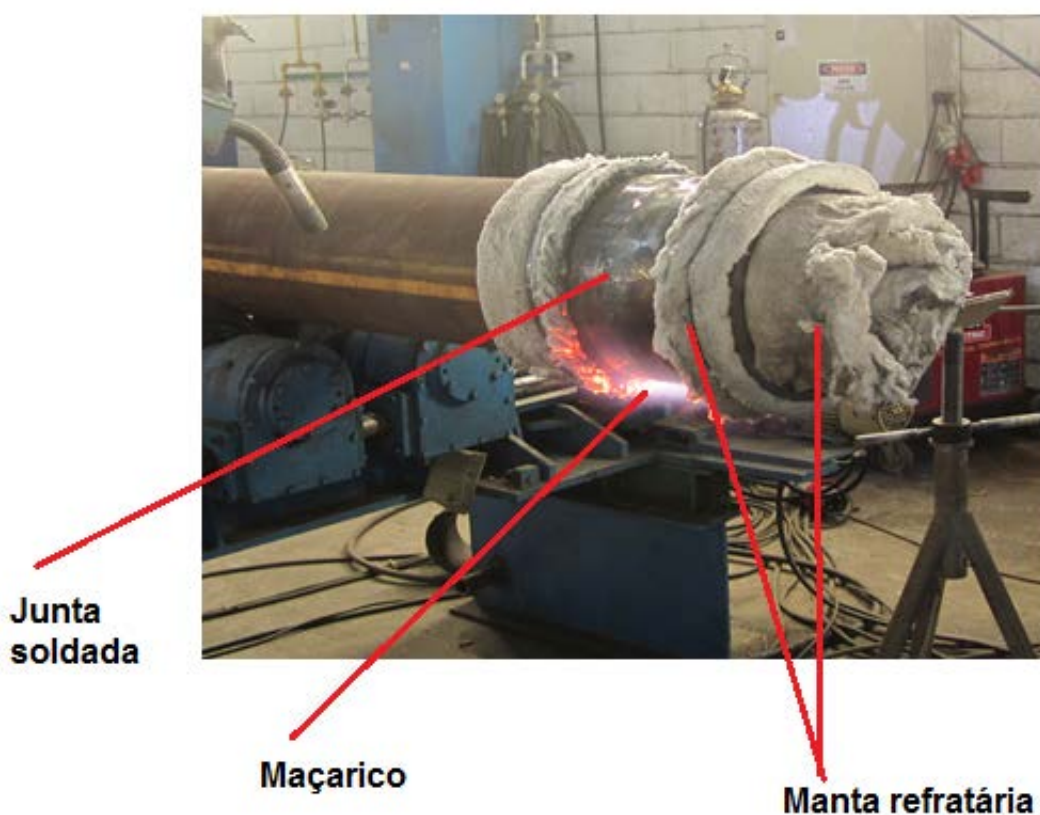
Conclusão da soldagem da peça de teste e pós-aquecimento.
